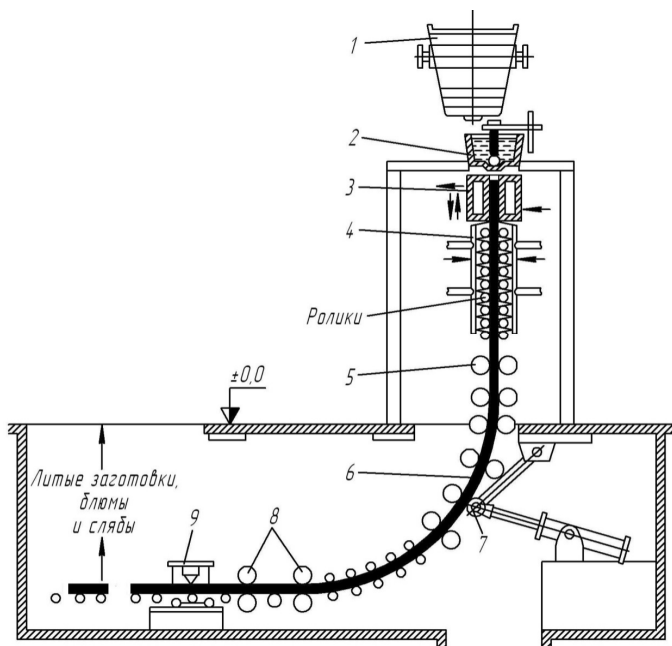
Схема машины непрерывного литья заготовок радиального типа: 1 – ковш с жидким металлом; 2 – промежуточный ковш; 3 – медный водоохлаждаемый кристаллизатор; 4 – система вторичного охлаждения; 5 – поддерживающие и тянущие ролики; 6 – непрерывно литой слиток; 7 – изгибающий ролик; 8 – правильно-тянущие ролики; 9 – передвижное устройство для поперечной резки горячей заготовки
